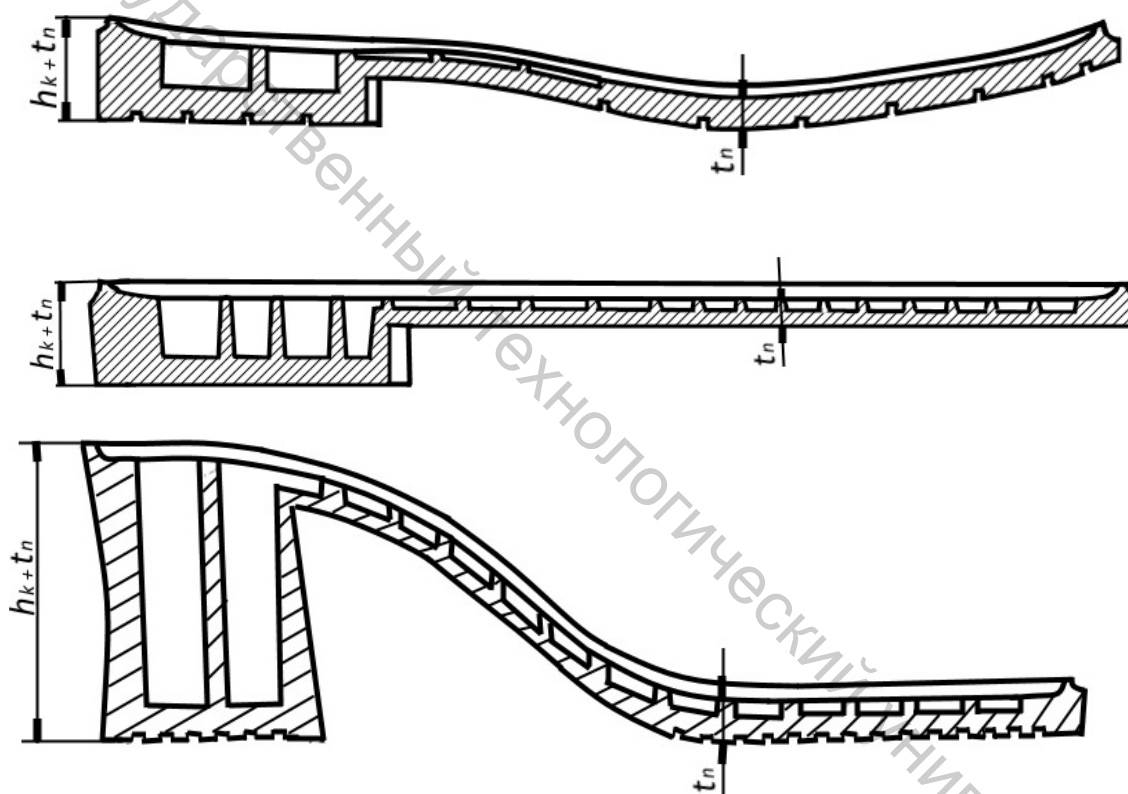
Пример оформления продольно-осевых разрезов подошв
